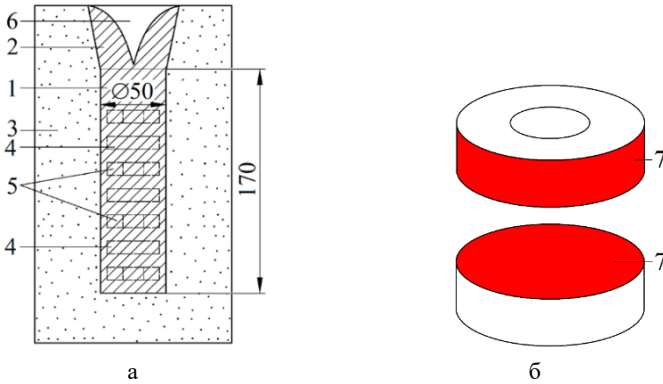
Схема вилівка у ливарній формі та вирізки зразків: 1 – вилівок; 2 – надставка; 3 – ливарна форма; 4 – зразки для визначення коефіцієнту тертя; 5 – зразки для визначення зношування; 6 – усадкова раковина; 7 – робочі поверхні зразків (зафарбовано червоним кольором).
